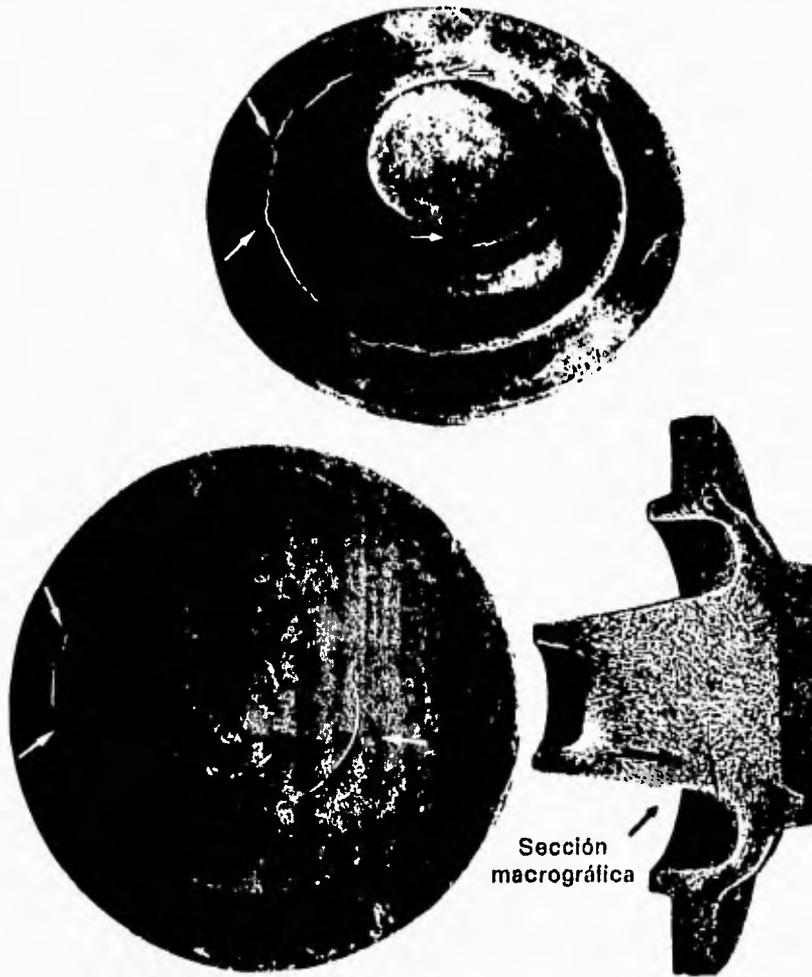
Grietas de temple en discos de acero estampados.
